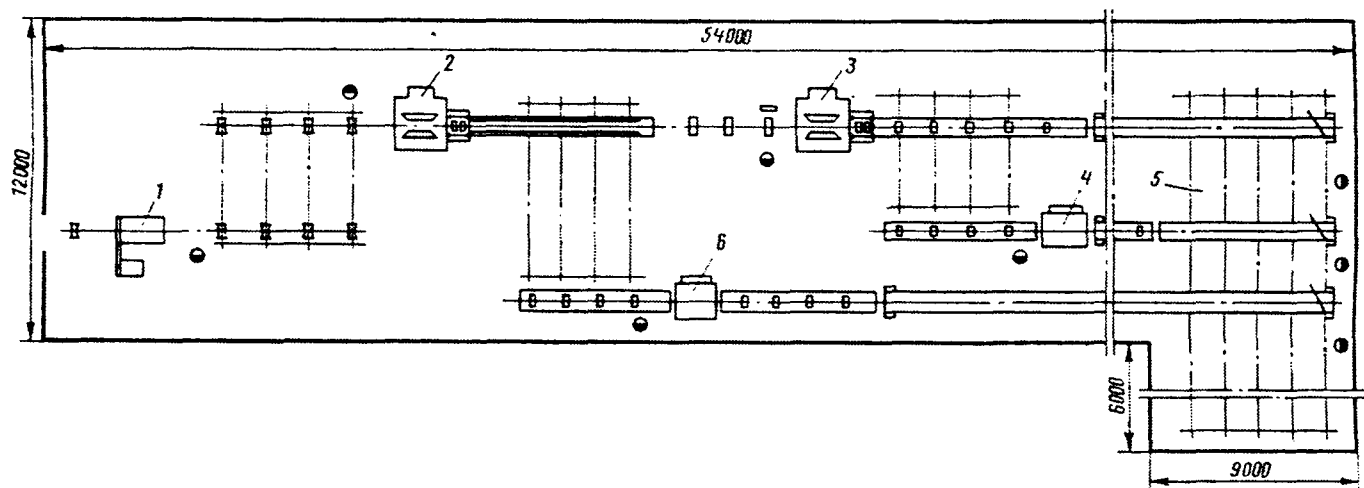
Схема технологического цеха с фрезернопильными и фрезерно-обрезными станками:
